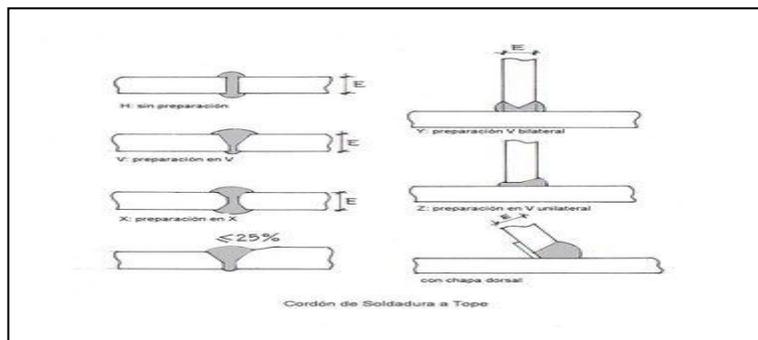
Dimensiones fundamentales de una soldadura
